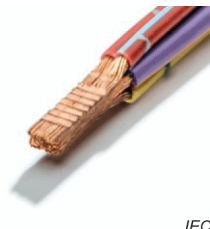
Connexion d'extrémité soudée par ultrasons
